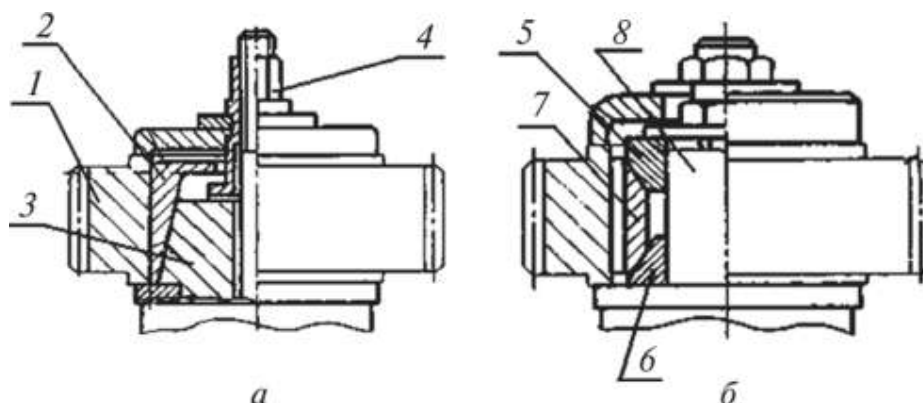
Схеми пристроїв із жорсткими розтискними втулками для зубофрезерних верстатів
